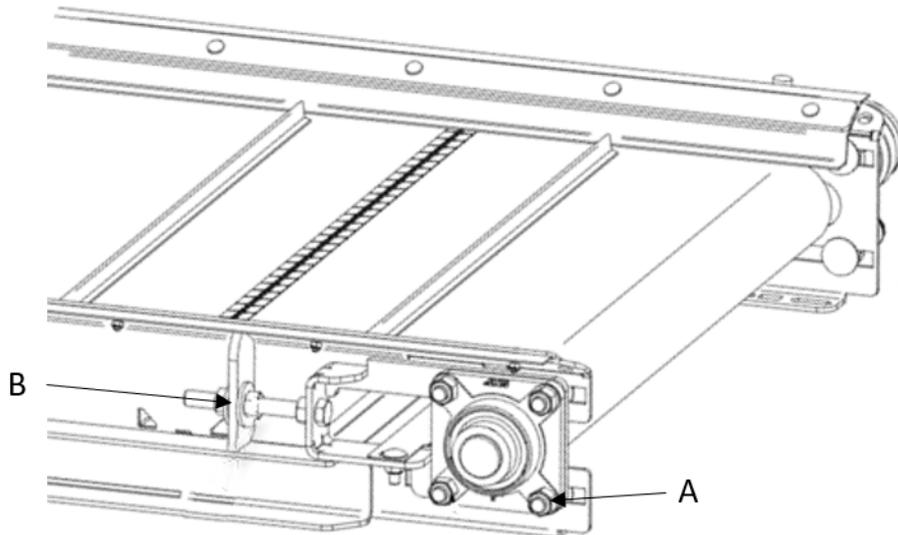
Réglage de la tension du tapis du convoyeur horizontal ou incliné
